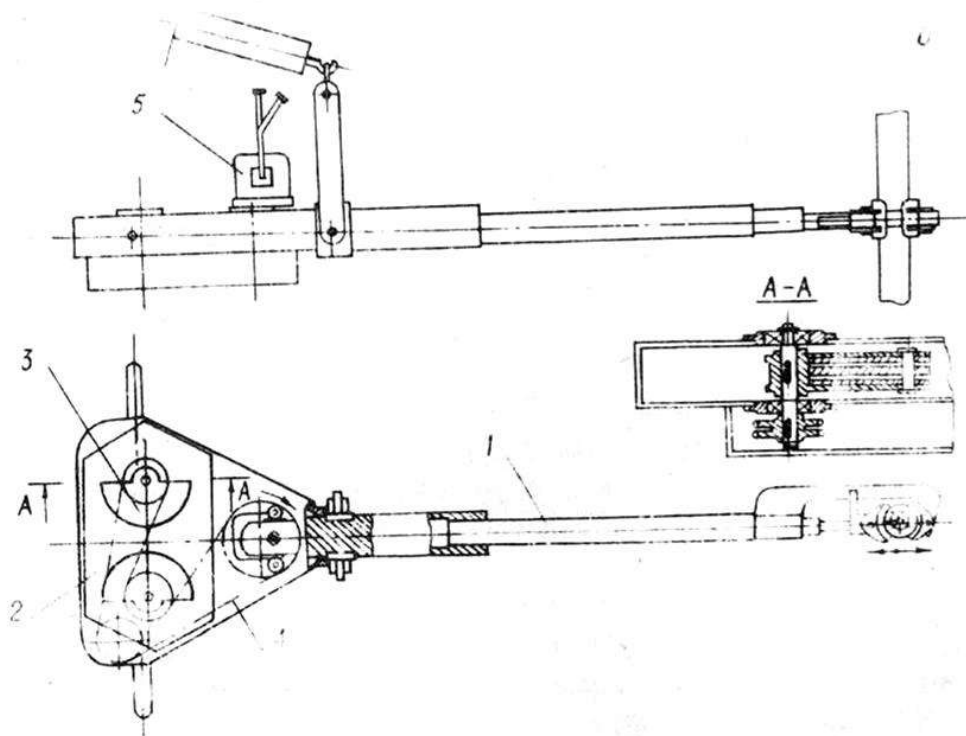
б. Встряхиватель для уборки плодов облепихи двухдебалансный:
